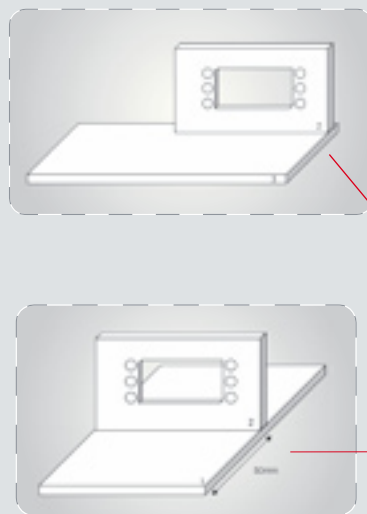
Assemblaggio delle parti che compongono un piede.
